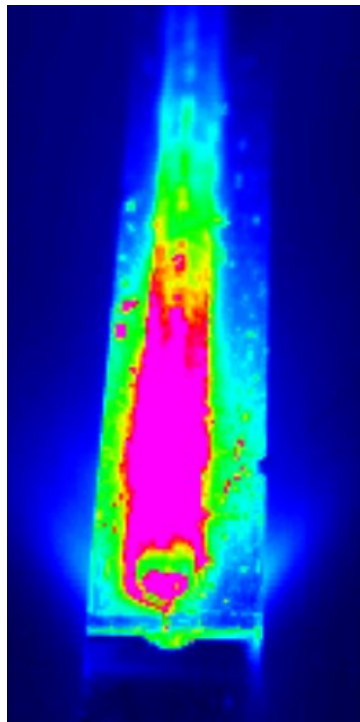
Imagem capturada com câmera de alta velocidade durante soldagem sobre chapa.
